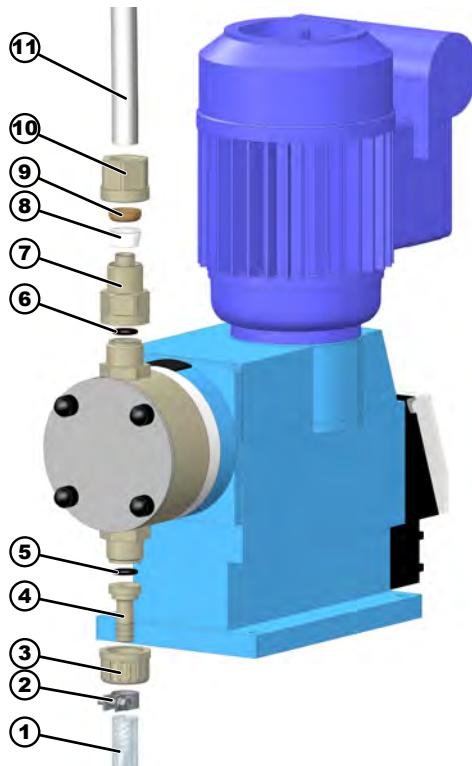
Montage Pumpenanschlussset EMP III Pumpe (54 l/h)
